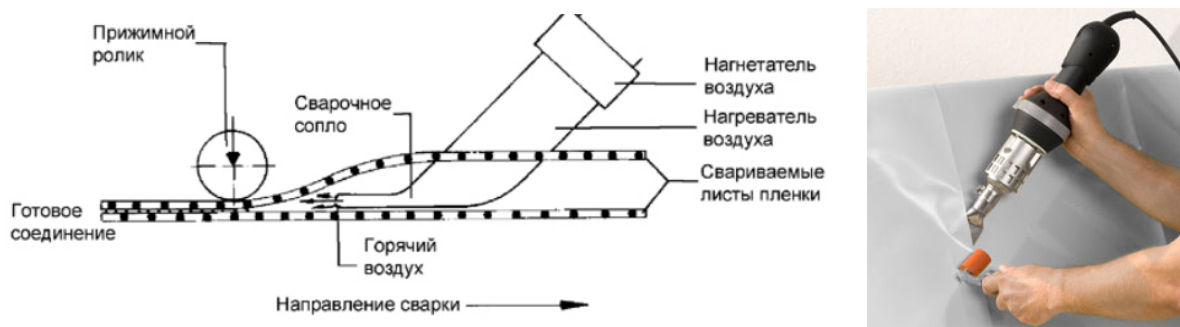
Сварка полимерных пленок горячим воздухом
